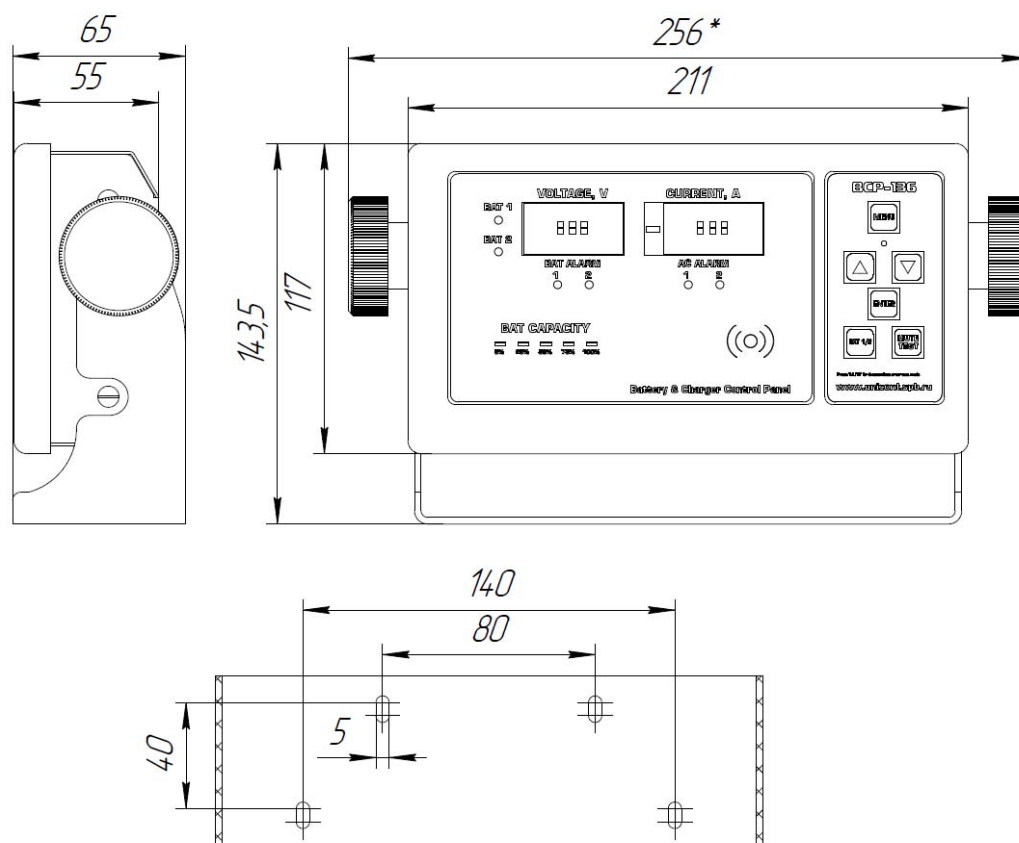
Габаритные и установочные размеры VCP-136 для крепления на поверхность
